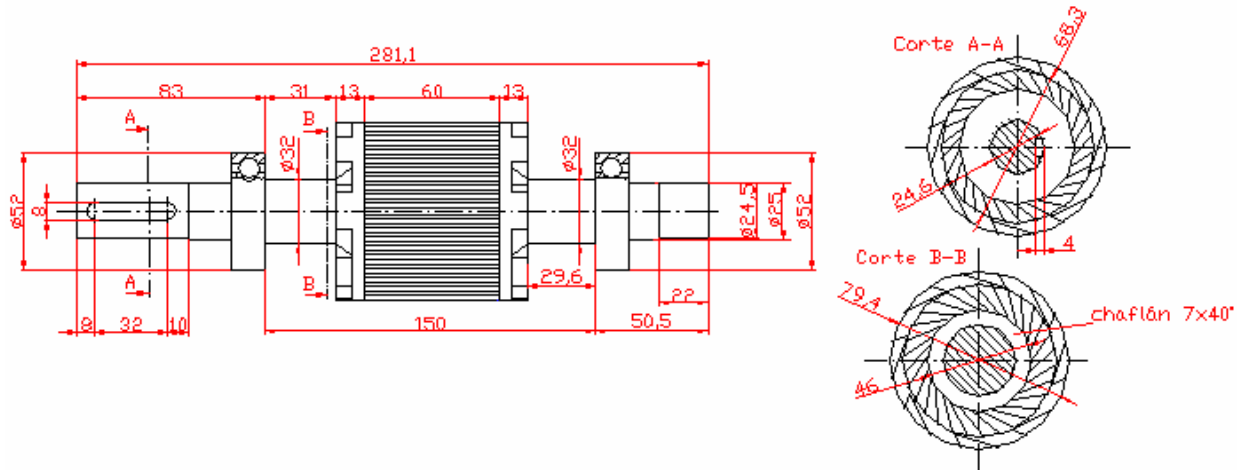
Vista lateral y en planta del rotor de chapas tipo *E*. Las cotas están dadas en mm.
